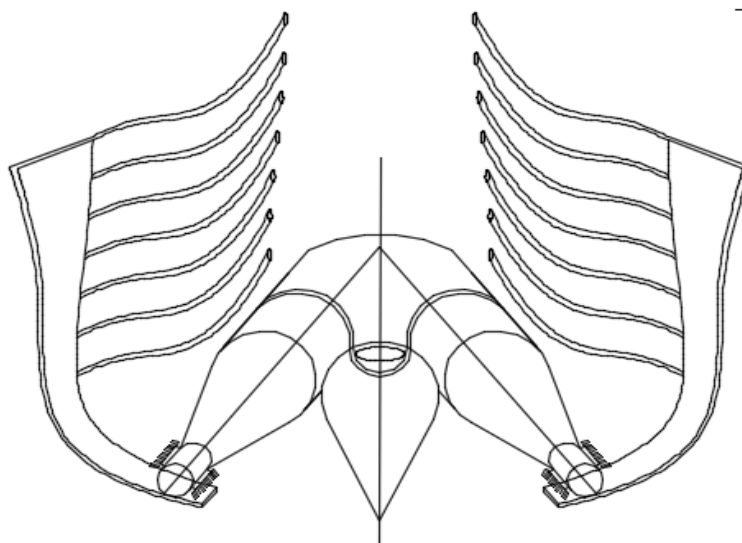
Кореневикопувальний пристрій, фронтальний вид
